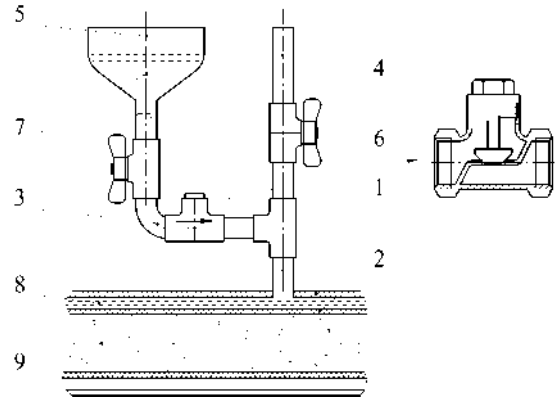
Пристрій для автоматичного поповнення робочої рідини: 1 – корпус гідравлічного компенсатора; 2 – трубчаста гумотканнна діафрагма; 3 – зворотний клапан; 4 – трубка для випуску повітря; 5 – місткість для робочої рідини; 6, 7 – шарові крани; 8 – робоча камера компенсатора; 9 – магістраль із розчинною сумішшю
